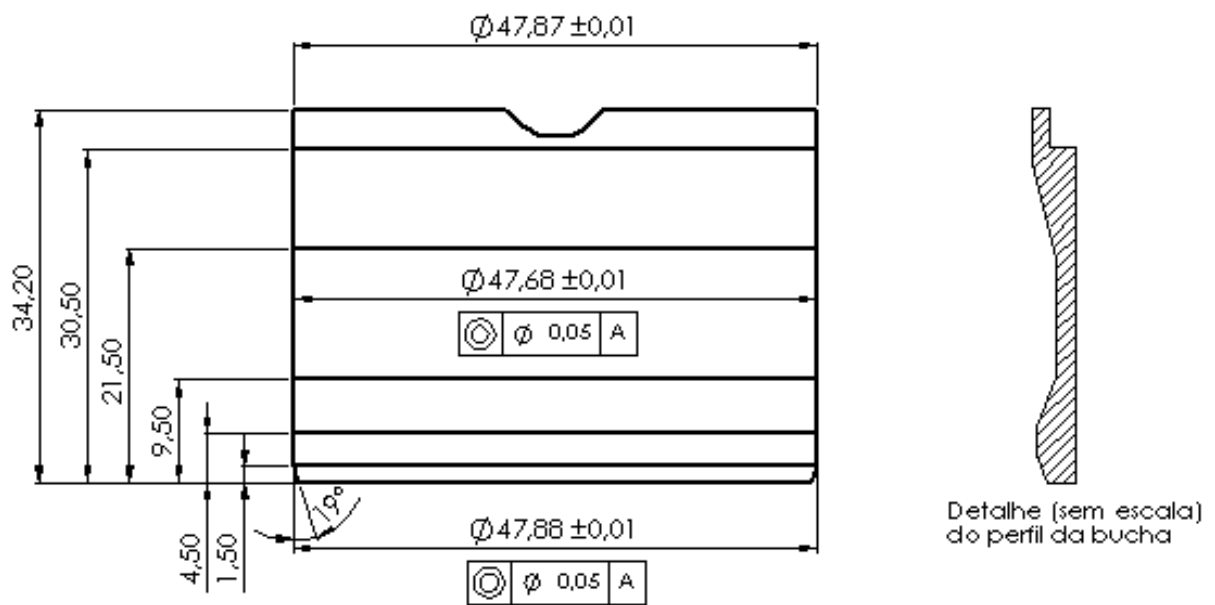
Desenho detalhado da bucha com detalhe do perfil em mm
